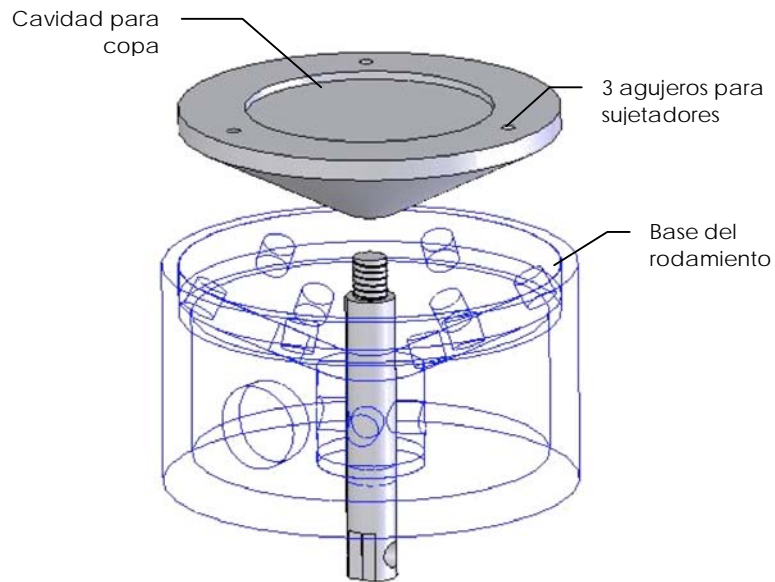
Vista explosiva del elemento flotante del cojinete neumático
